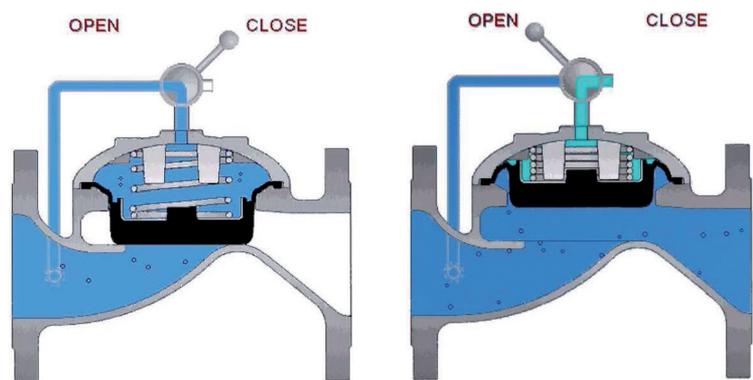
Válvula hidráulica seccionada cerrada y abierta. Fuente Bermad.
